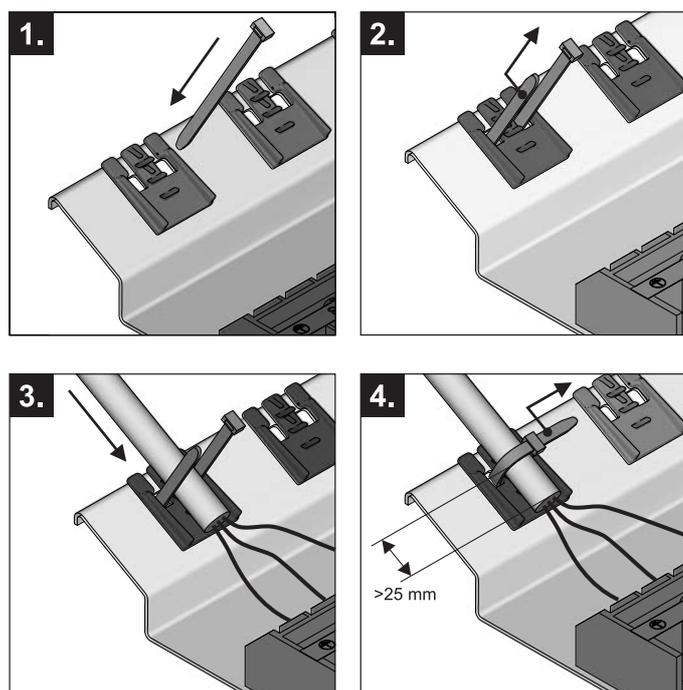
Encaixar o clipe de fixação e apertar os cabos com o agrupador
